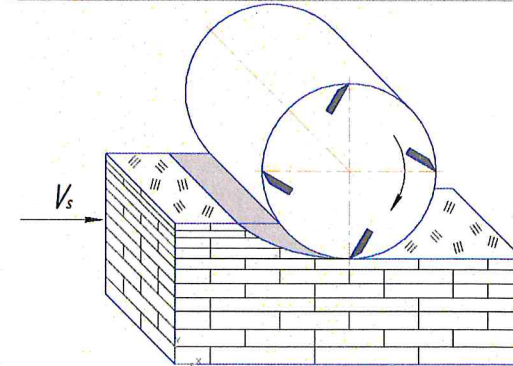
Схема снятия припуска древесностружечной плиты винтовой фрезой с возможностью регулирования фракций изменением количества зубьев фрезы.
